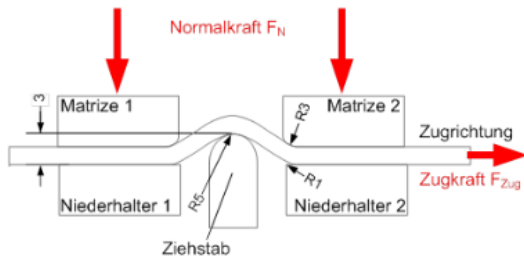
Versuchswerkzeug mit Ziehsickengeometrie
